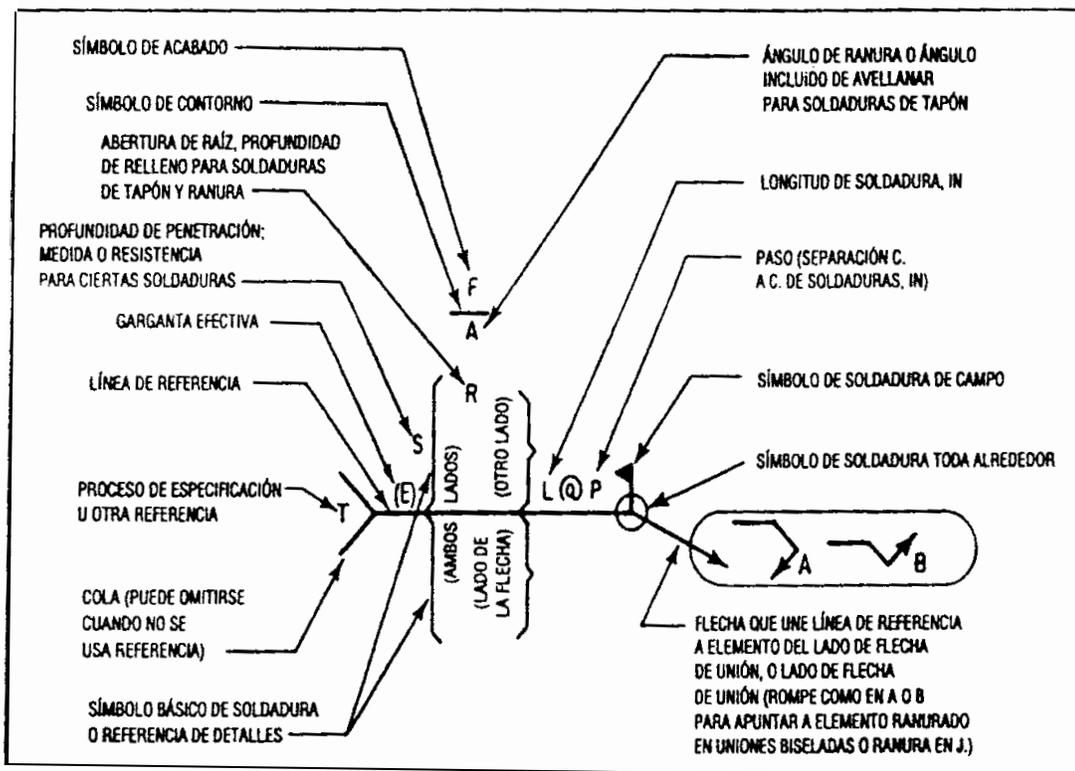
Ubicación estándar de elementos de un símbolo de soldadura.
